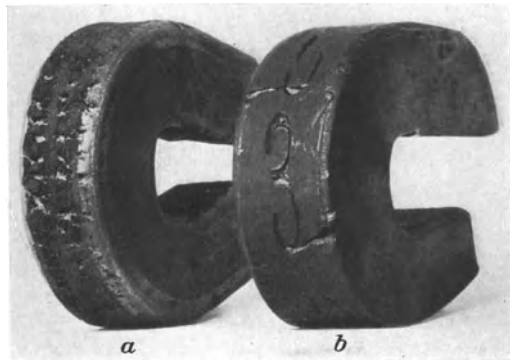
Biegeproben mit metallischen Anbrüchen: *a* infolge Oberflächenanrisse, durch zu heißes Schmieden entstanden. *b* infolge Verletzungen von tief eingeschlagenen Zahlen. Werkstoff St. 38:13.
